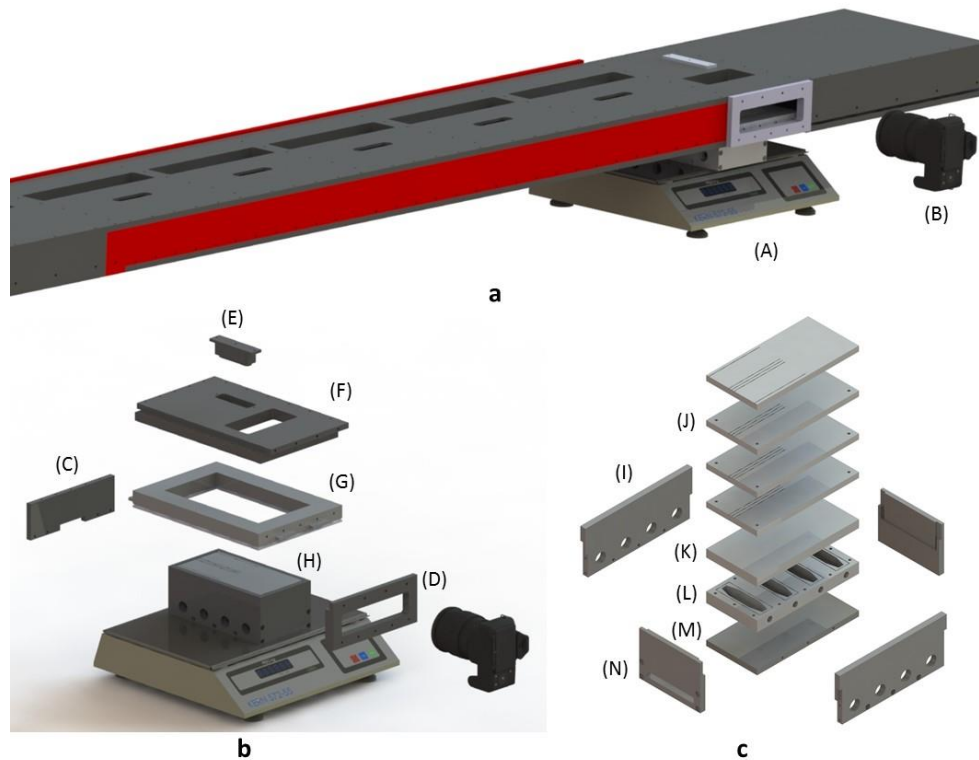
a : Vue d'ensemble de la veine d'essais assemblée – b : Détail du module *Glace
